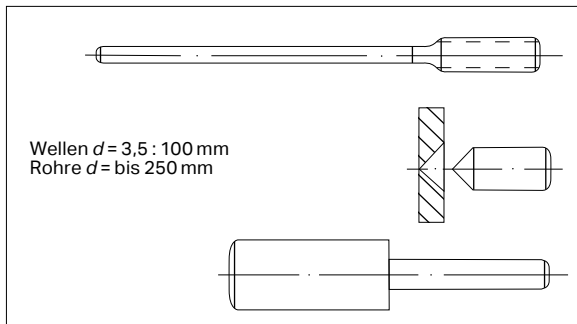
Prinzip des Gaspressschweißens ⁽¹²⁾
